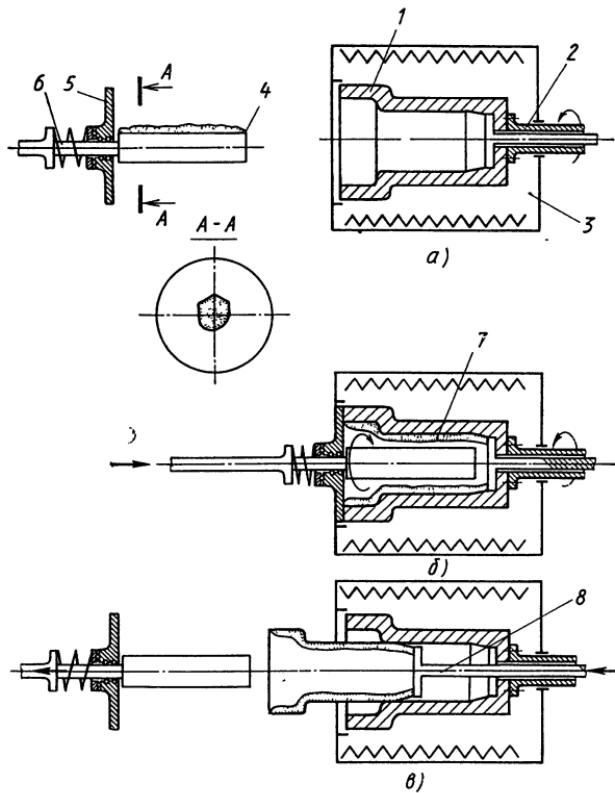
Центробежный метод изготовления оболочковых стержней:
